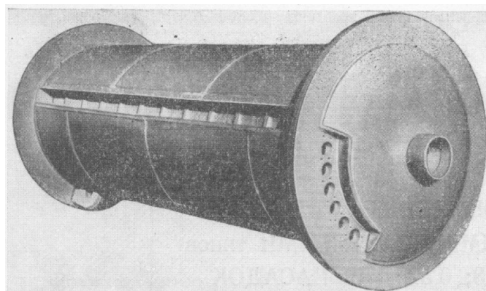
Конструкция разработанного сварного ПТА
